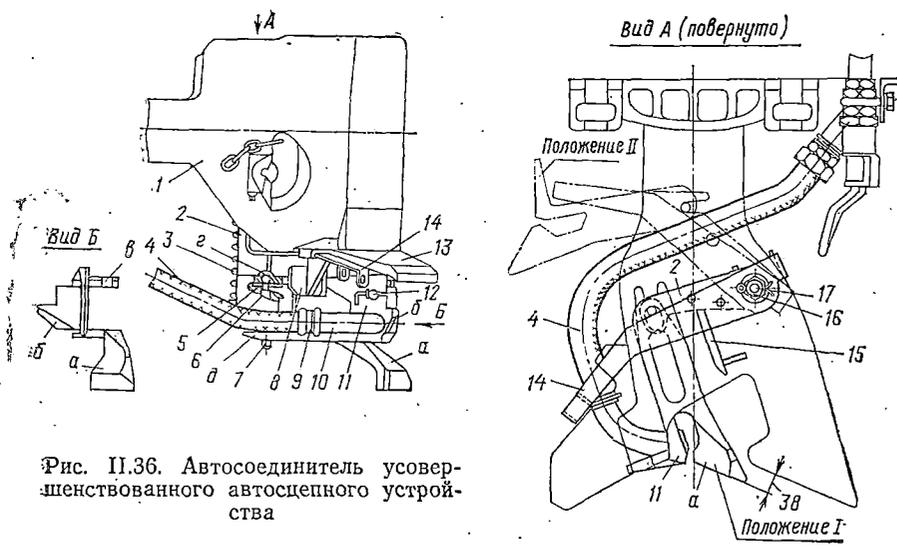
Автосоединитель усовершенствованного автосцепного устройства
